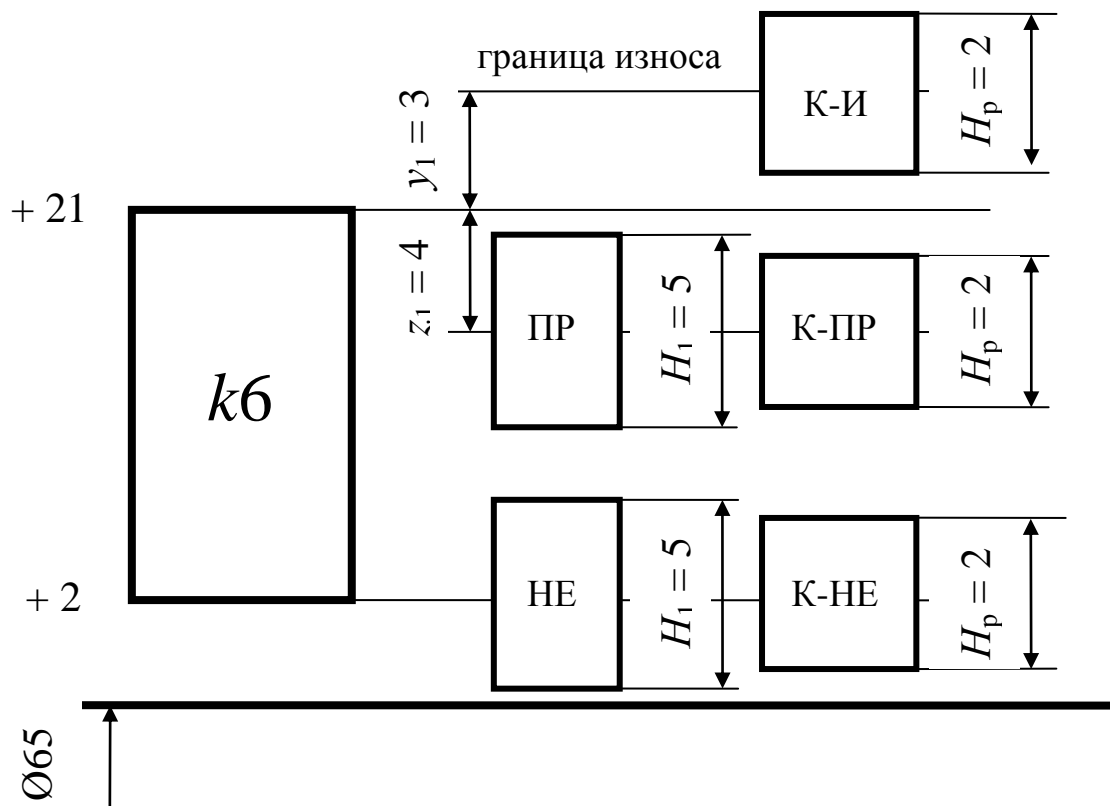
Схема расположения полей допусков калибров для контроля вала  $\varnothing 65k6$
